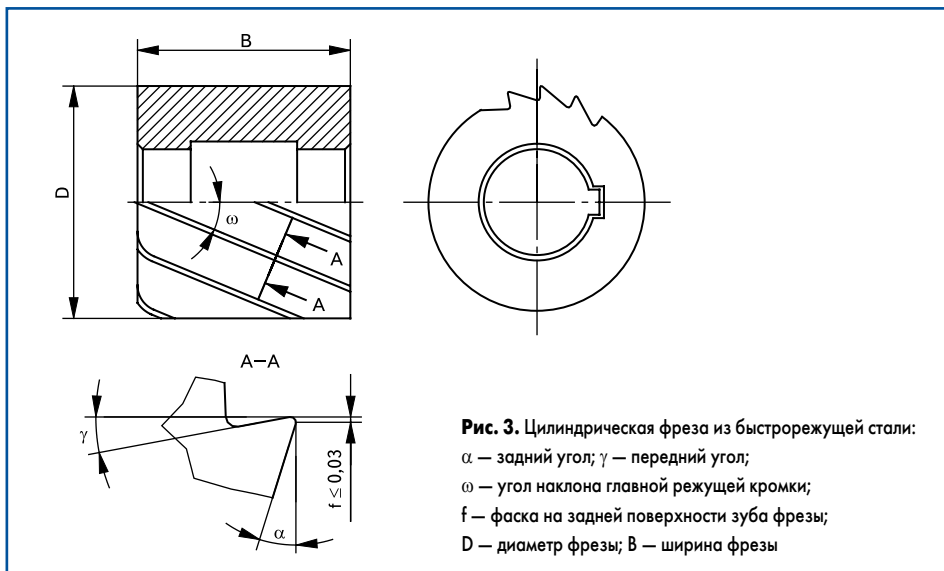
Цилиндрическая фреза из быстрорежущей стали:
